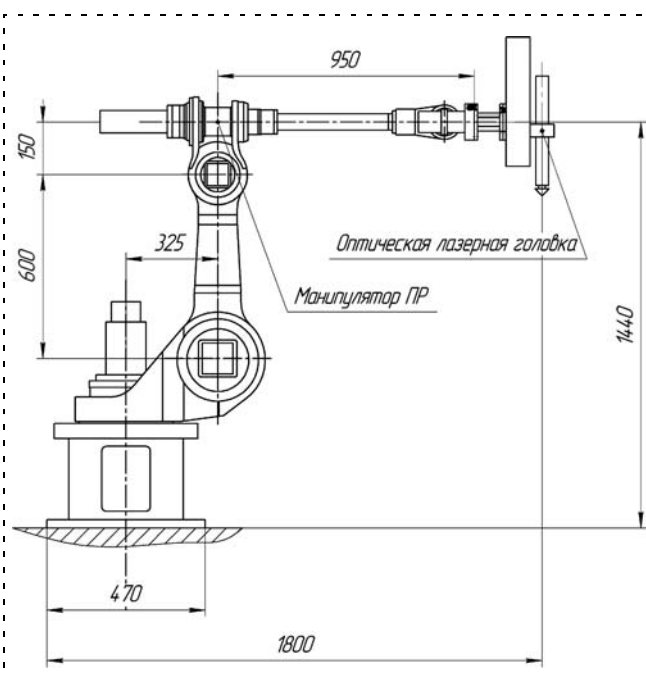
Манипулятор, входящий в состав РТК лазерной сварки
